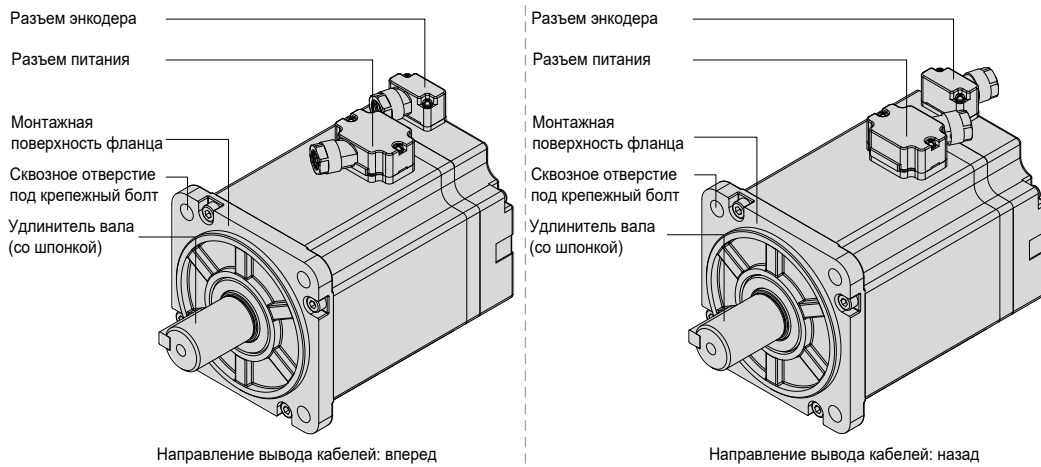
Узлы и детали электродвигателей с клеммной коробкой серии MS1
